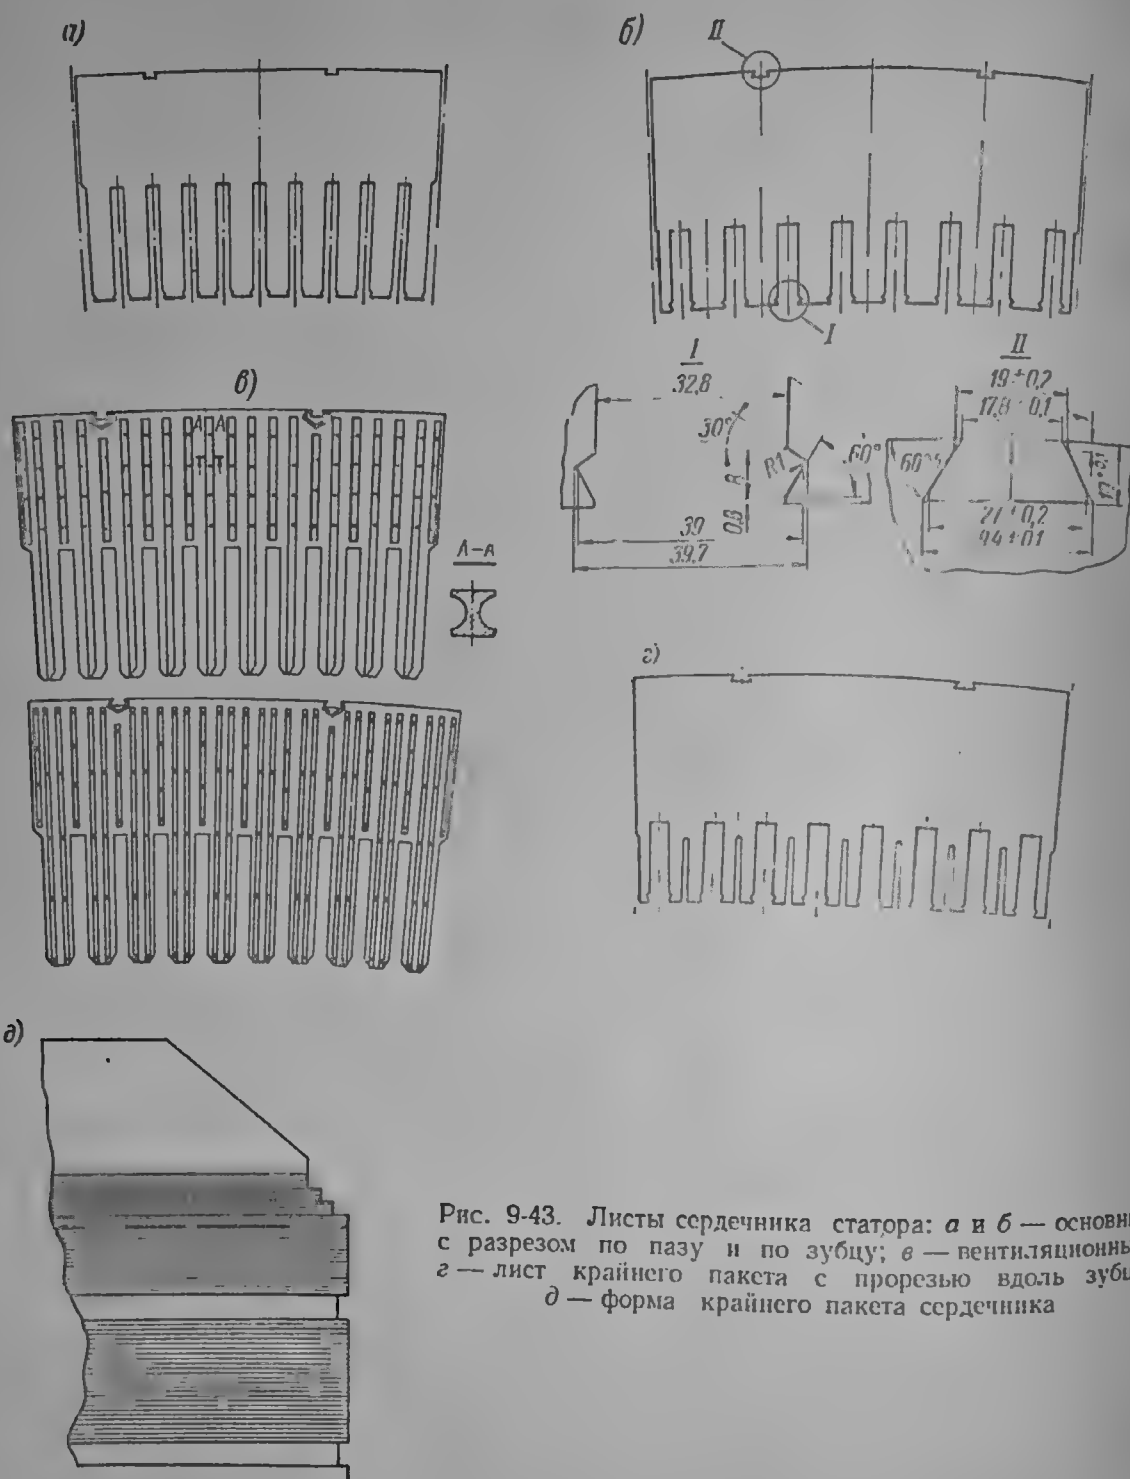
Листы сердечника статора: а и б — основные с разрезом по пазу и по зубцу; в — вентиляционные; г — лист крайнего пакета с прорезью вдоль зубца; д — форма крайнего пакета сердечника
